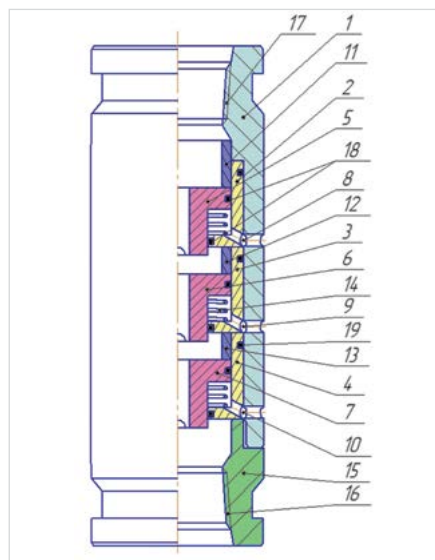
Забойный гидромеханический компенсатор: 1 — корпус; 2, 3, 4 — перегородки; 5, 6, 7 — поршни; 8, 9, 10 — каналы связи с затрубьем; 11, 12, 13 — втулки; 14 — пружины; 15 — переводник; 16, 17 — присоединительные резьбы; 18, 19 — уплотнения
